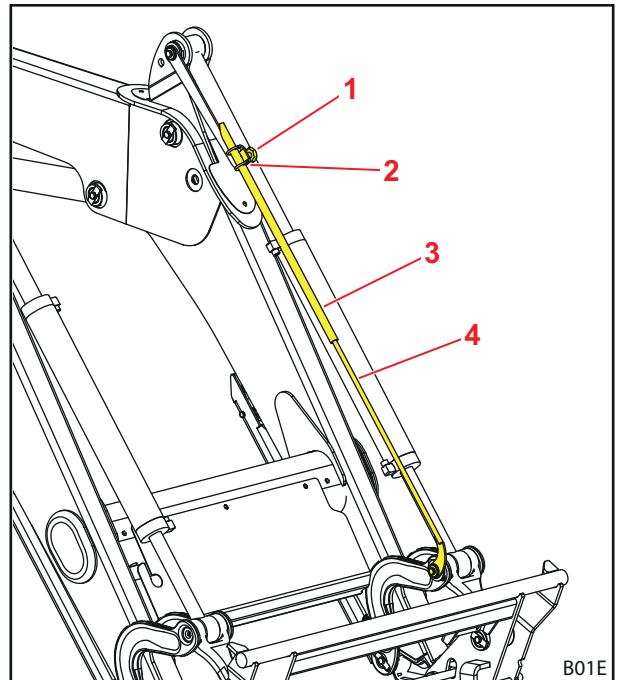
Indicateur visuel pour l'ajustage d'outil
